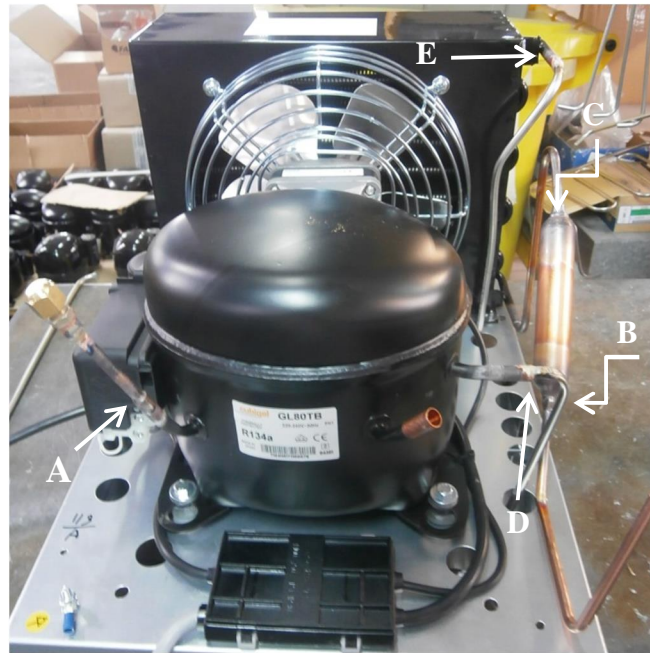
Operações de soldadura na mesa de trabalho
